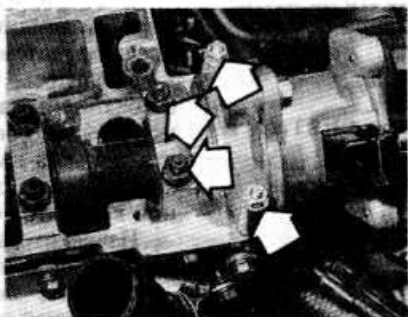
Гайки крышки подшипника распредвала (стрелки) — двигатель с двумя распредвалами
